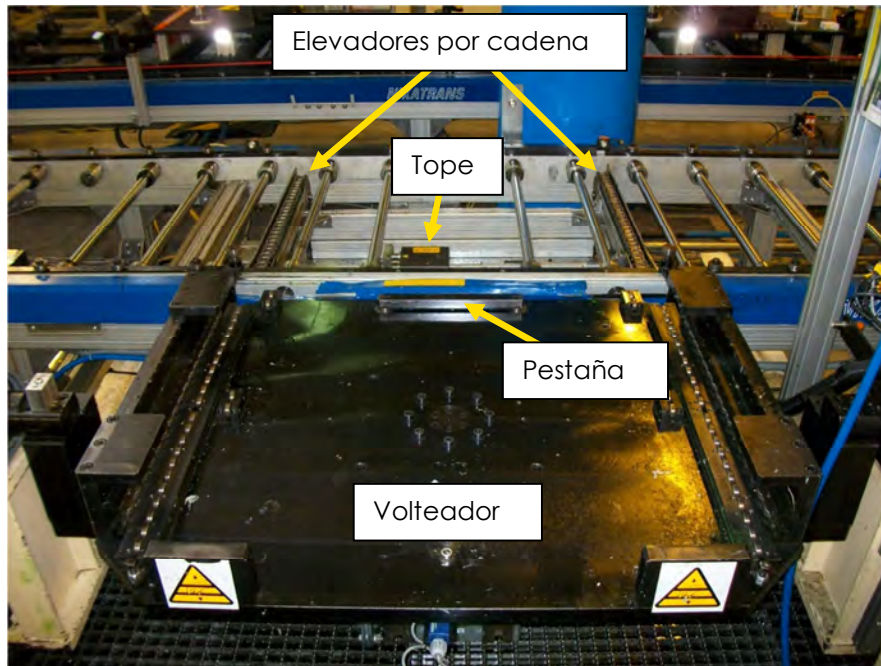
A VOLTEADOR Y ELEVADOR DEL PUESTO DE MONTAJE FINAL
